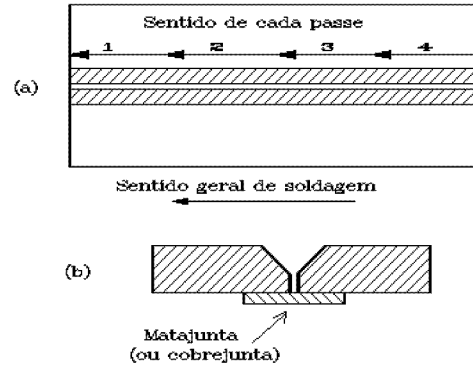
Técnicas de Soldagem para Minimizar a Deflexão Magnética do Arco.
